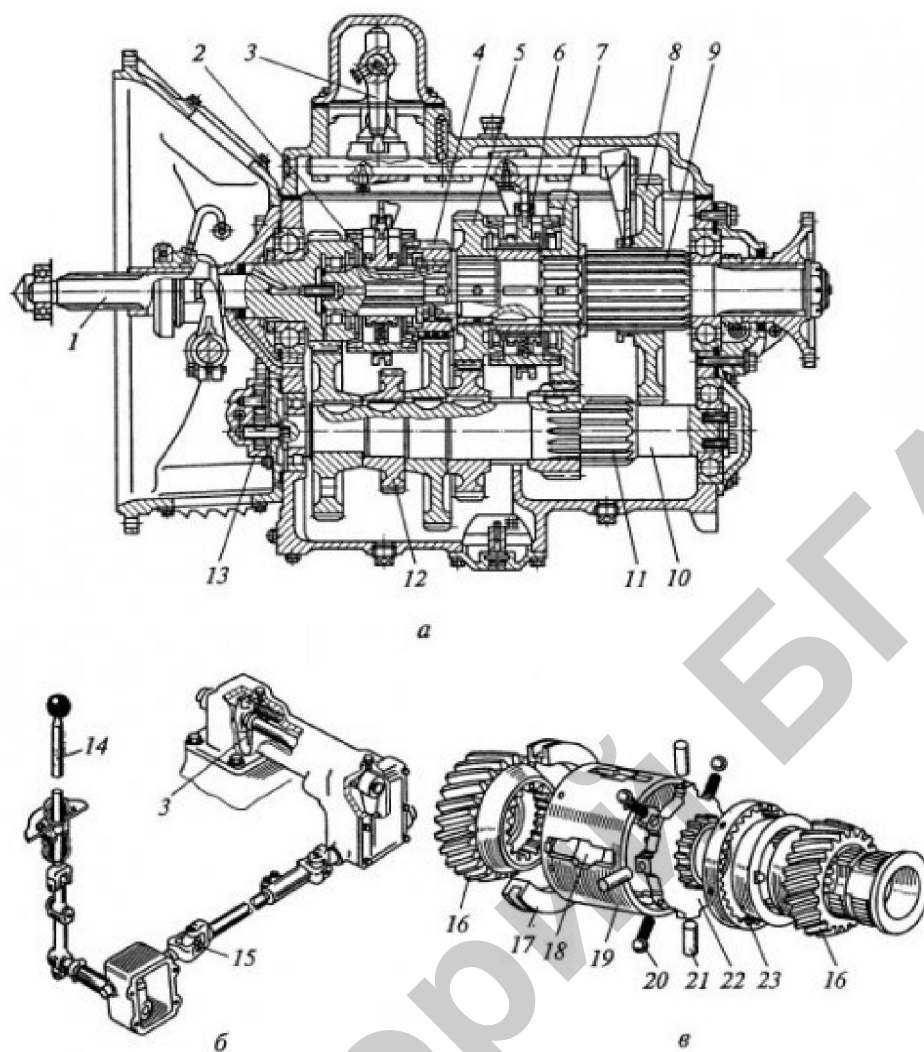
Коробка передач грузовых автомобилей МАЗ:
